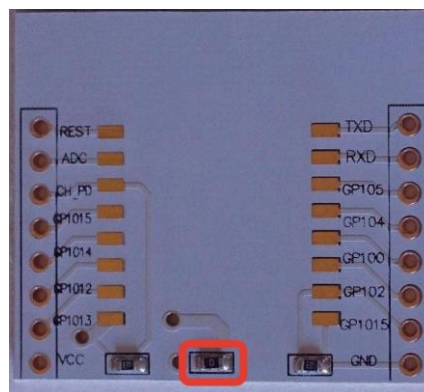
Резистор для вибору джерела живлення на макетній платі з ESP8266-12F
